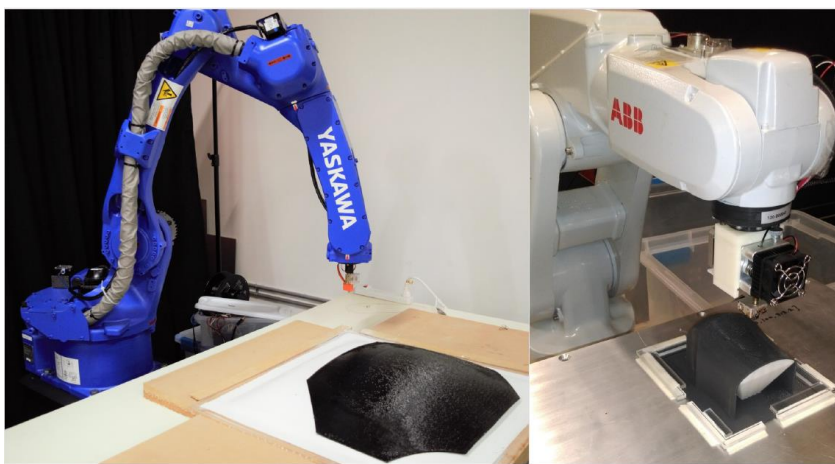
Printare cu robot Yaskawa și ABB [40]
